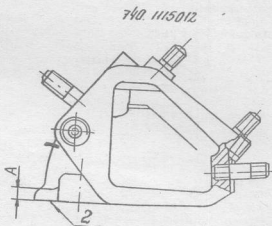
Патрубок соединительный впускных коллекторов в сборе
